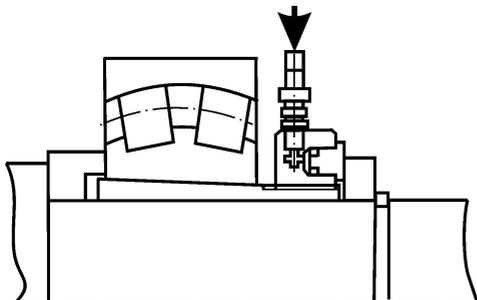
Разборка подшипников с закрепительной втулкой с применением гидравлической гайки и упорного кольца
